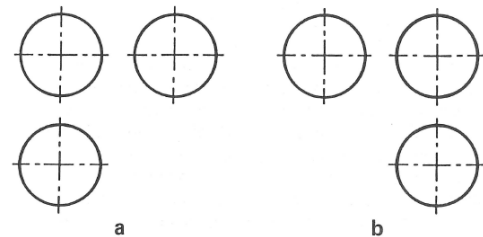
Ansichten einer Kugel [Ho86]
